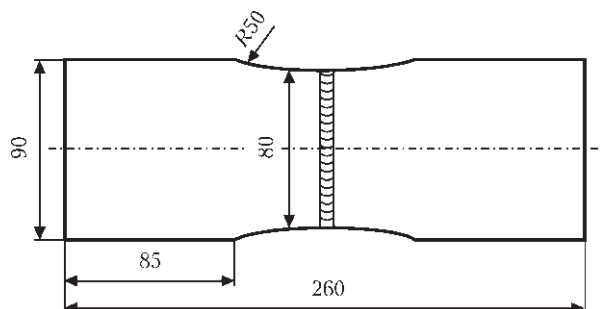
Форма и геометрические размеры сварных образцов для усталостных испытаний
